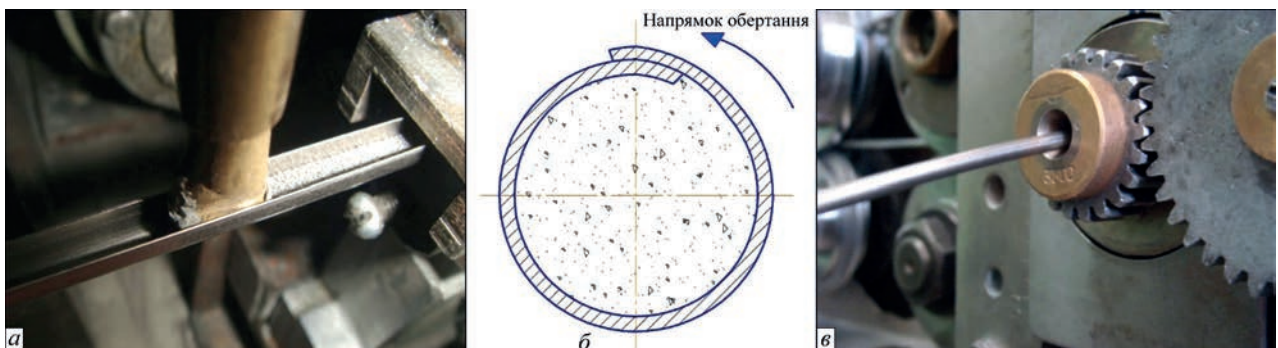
Процес формування та перетяжки металопорошкового дроту: а – дозування шихти; б – схема закриття оболонки; в – філь'ера, що обертається
